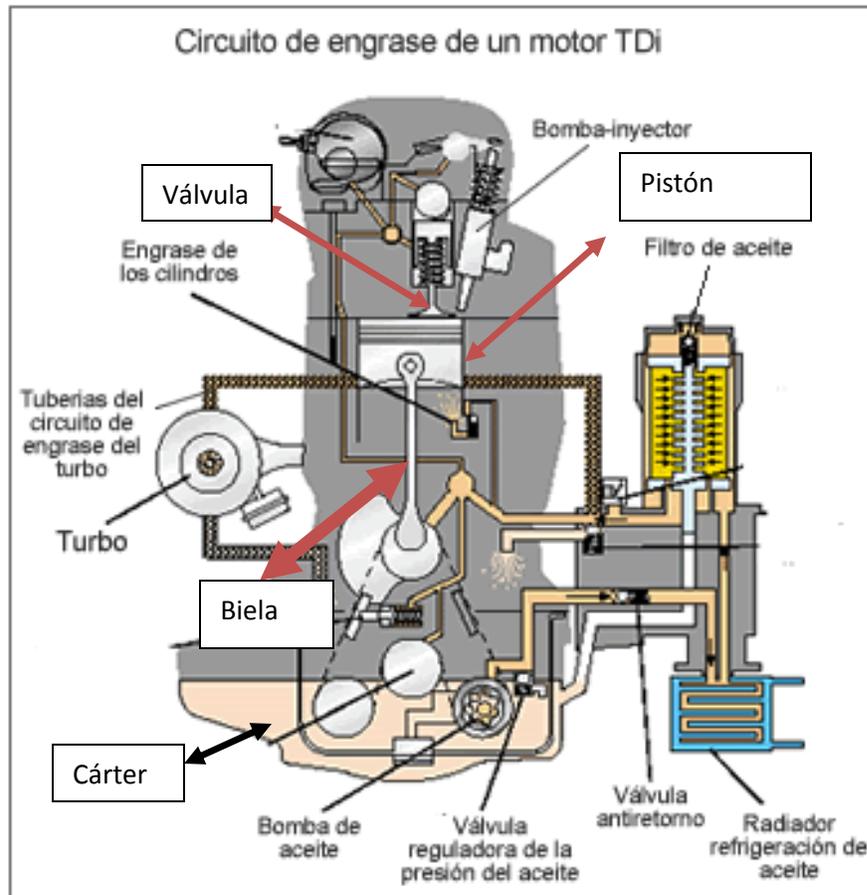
Circuito de engrase de un motor TDI con Turbocompresor
